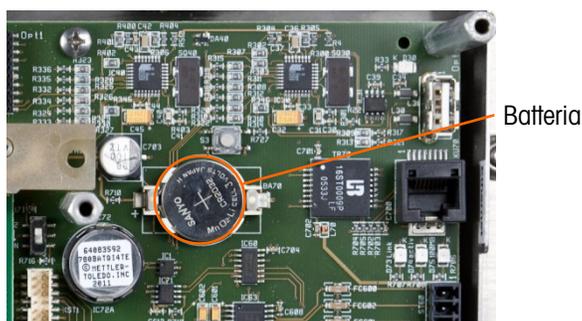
PCB principale, con indicazione della posizione della batteria
